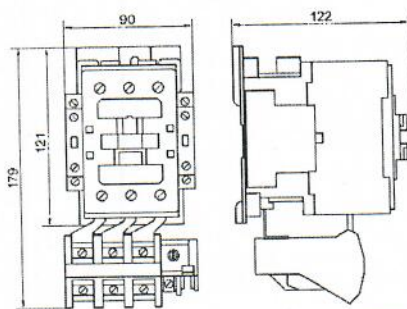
Пускатель неререверсивный ПМ12-063 63А вариант А. Степень защиты - IP20
